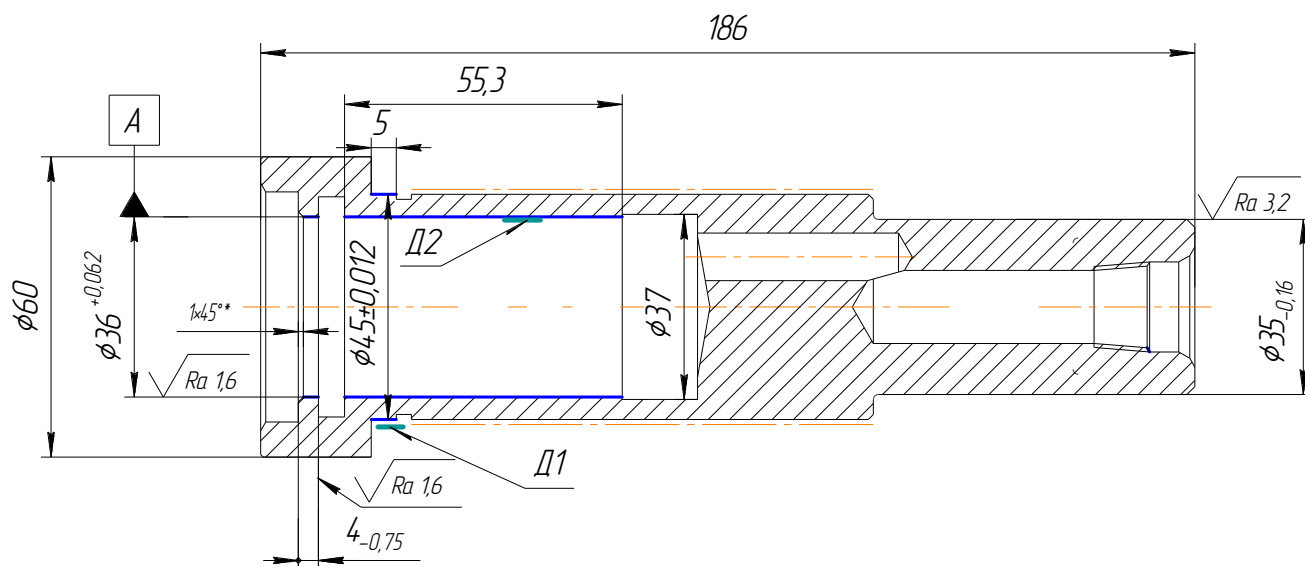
Ремонтне креслення корпусу гідроциліндра
